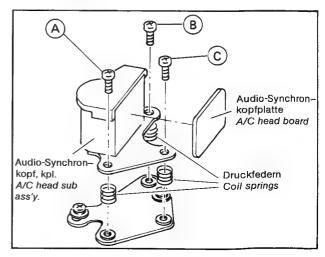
Synchronkopfausbau Fig. 2-3 A/C head replacement
